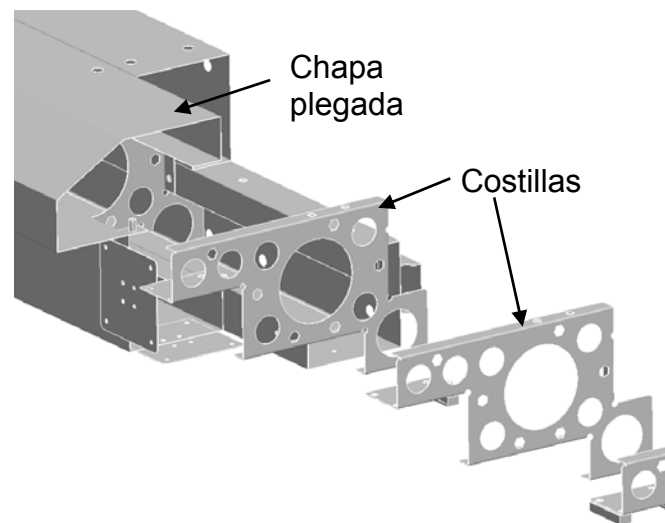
Solución constructiva del puente original (cortesía Roglan Equipment)
